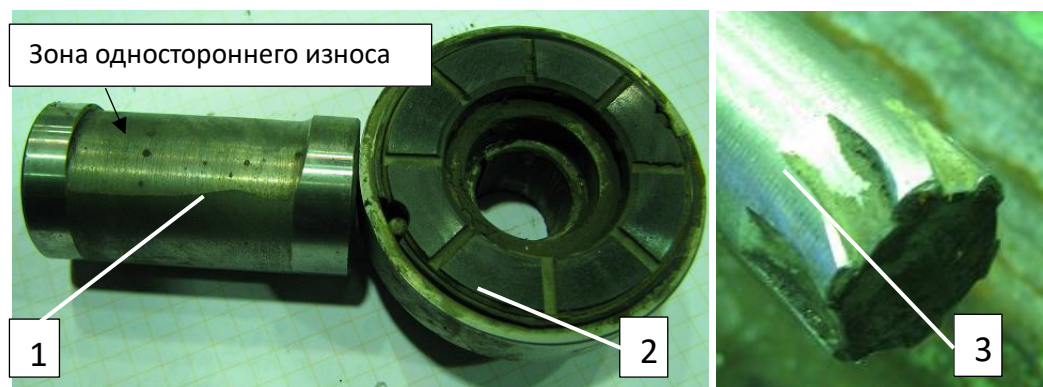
Общий вид изношенных деталей секции №14: 1 - втулка радиального подшипника, 2 - пята упорного подшипника, 3 - вал
